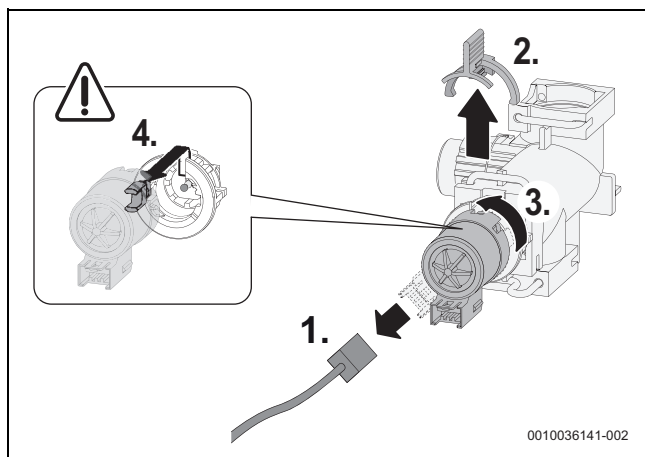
Separar el motor de la válvula de 3 vías (variante sin tornillos)
